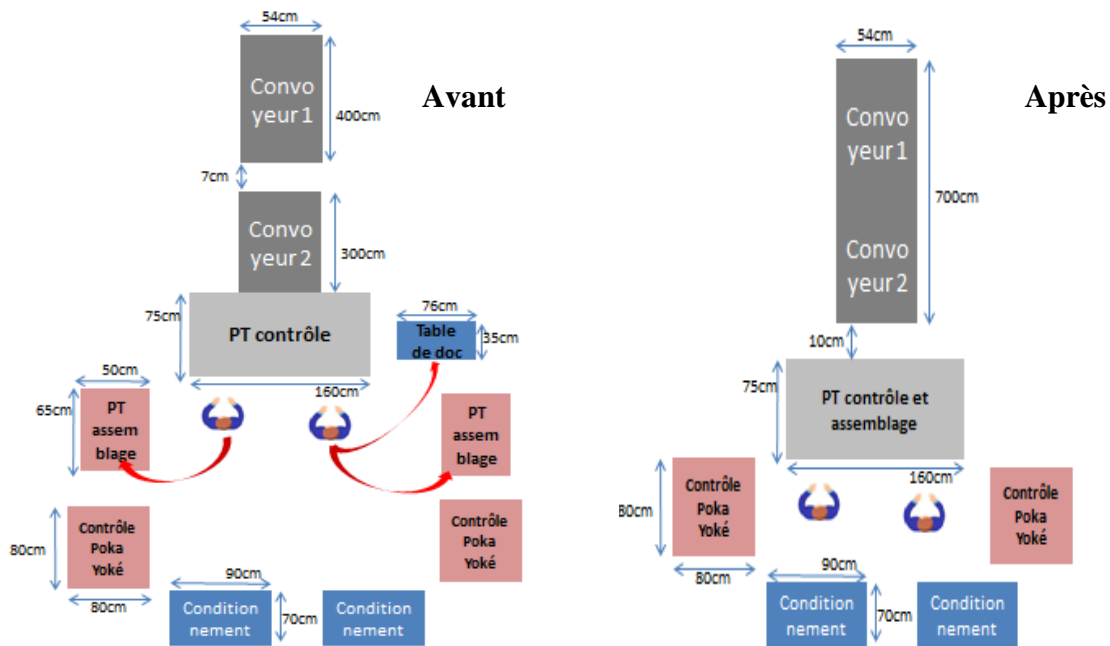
LAYOUT du B Pillar avant et après l'installation du nouveau PT
